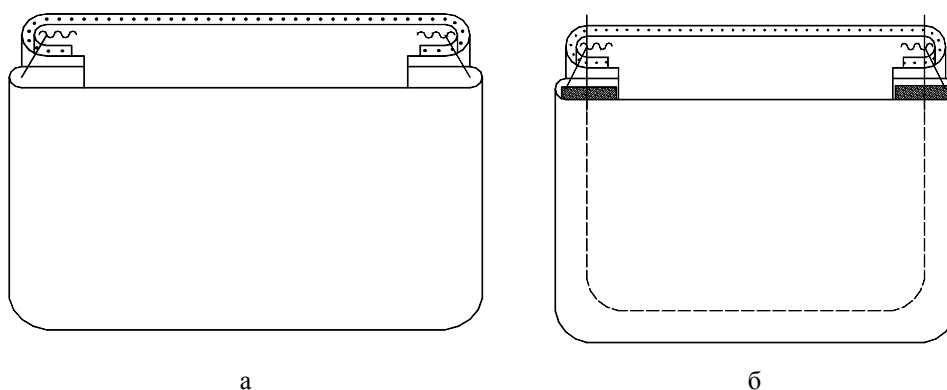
Монтажная схема конструкции клапана, обработанного обтачным швом
